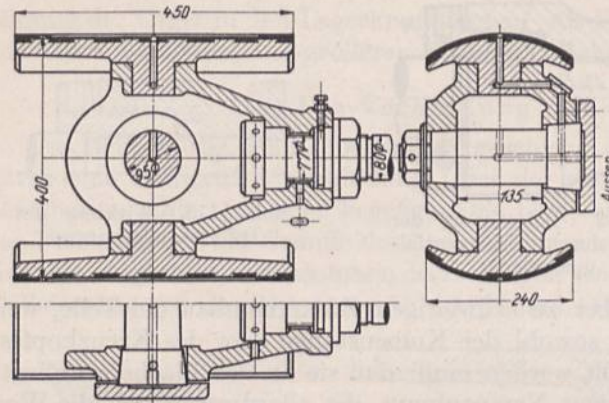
Kreuzkopf für Gleichstromdampfmaschinen, Prof. Stumpf.
